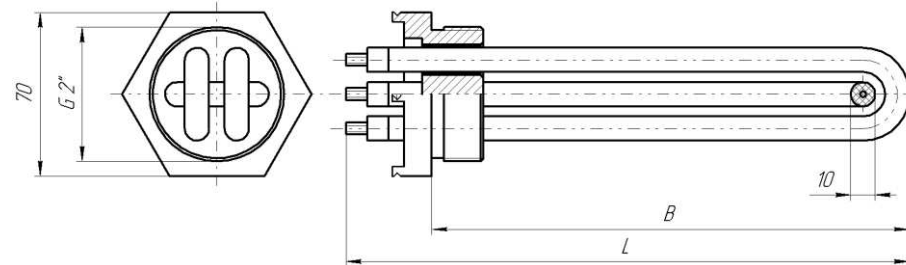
Трубчатый электронагреватель блочный ТЭНБ.
